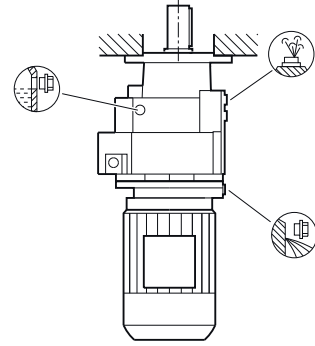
Düz dişli için montaj konumları DF/ZF Flanşlı model ve gövde flanşlı DZ/ZZ, Boyutlar 19 - 29
